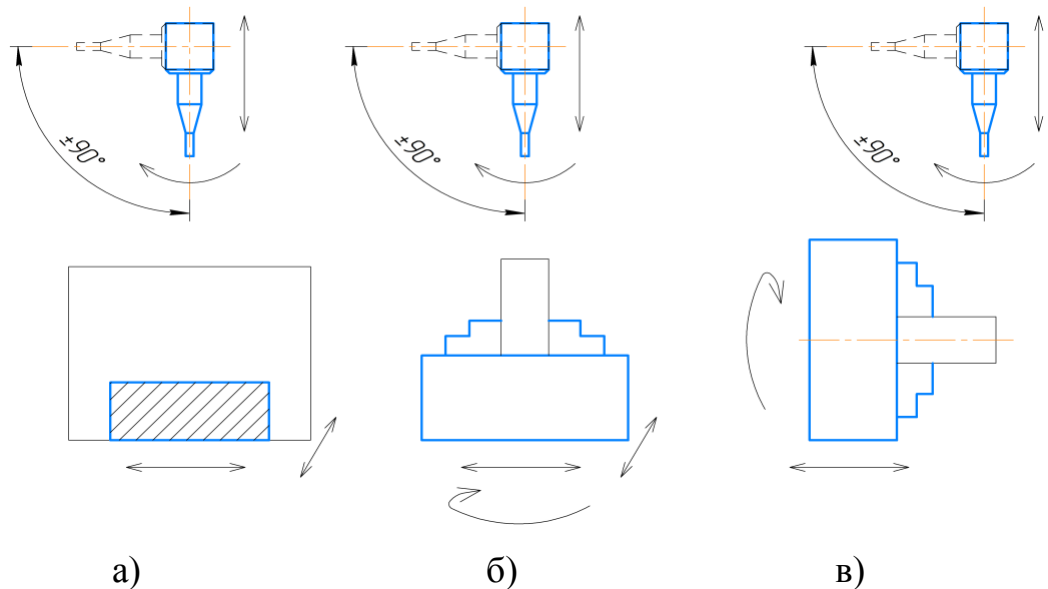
Вертикально-фрезерне компонування із закріпленням заготовки у: а - призматичних лещатах; б – трикулачковому патроні з вертикальною віссю обертання; в – трикулачковому патроні з горизонтальною віссю обертання
